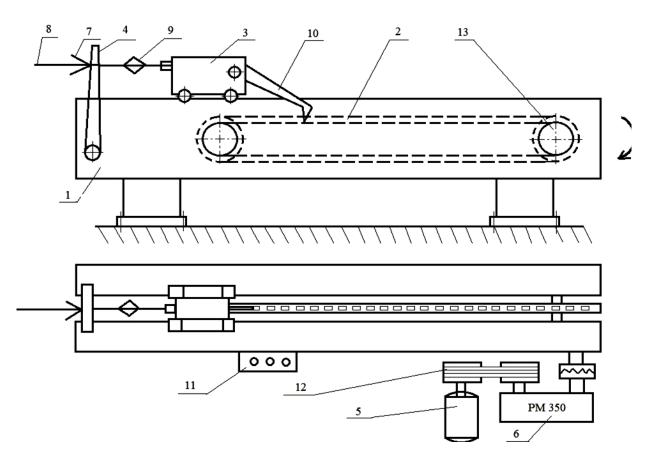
Цепной прямолинейный волочильный стан: 1 — станина; 2 — тяговая цепь; 3 — тележка с захватом; 4 — волокодержатель; 5 — двигатель; 6 — редуктор с муфтой; 7 — волока; 8 — проволока; 9 — захват; 10 — тяговый зацеп; 11 — пульт управления; 12 - клиноременная передача; 13 — тяговая звездочка.
